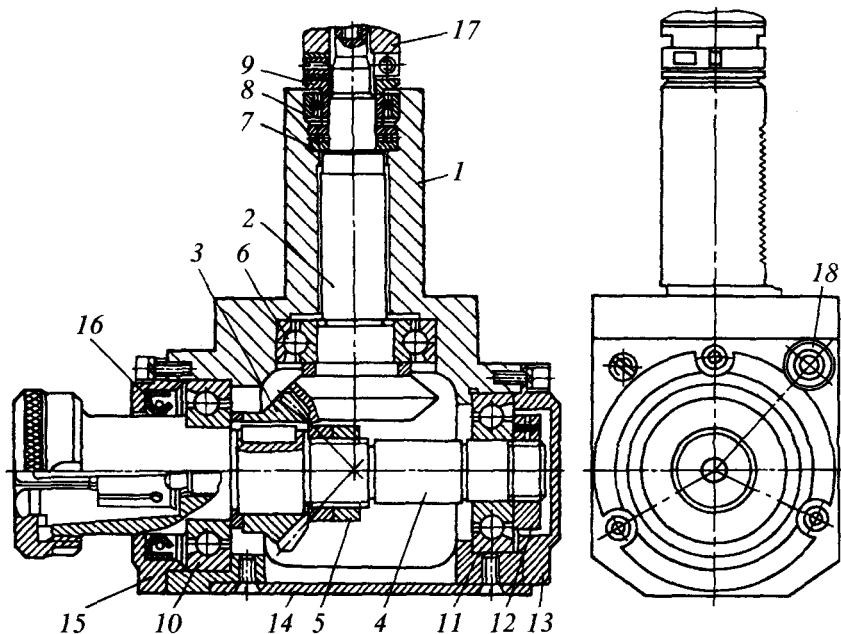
Державка для вращающегося инструмента с цанговым патроном
